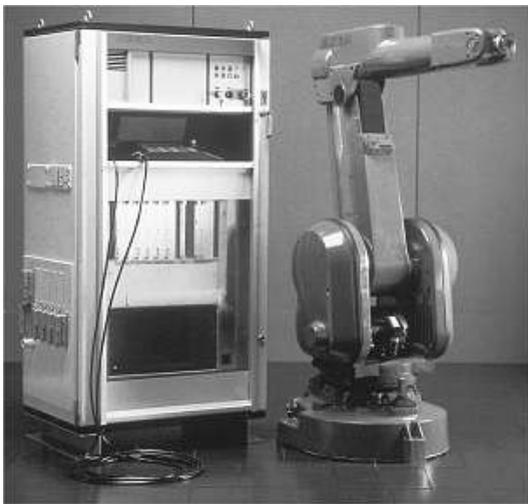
6-achsiger Roboter mit Steuerschrank [Quelle: ABB]
